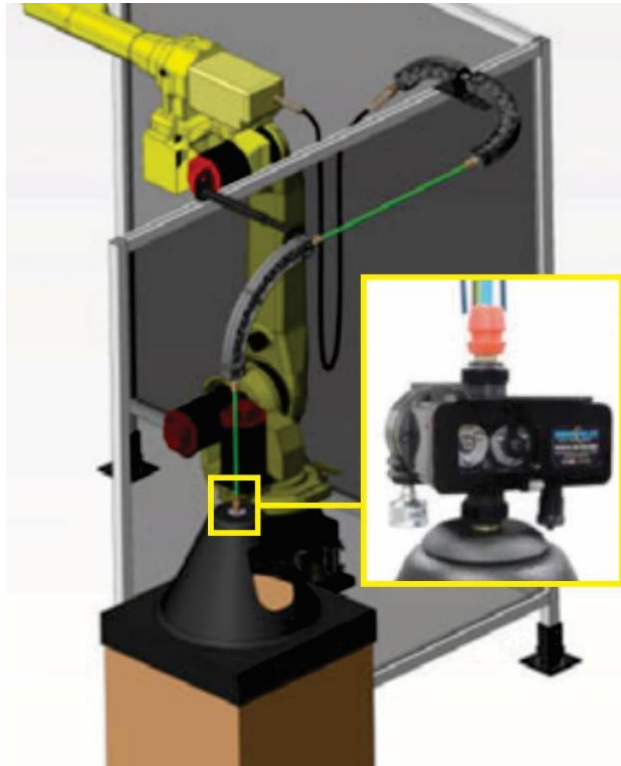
Tracionador pneumático em detalhe com indicação de local de instalação em circuito de alimentação de arame de célula de soldagem robotizada [43]
